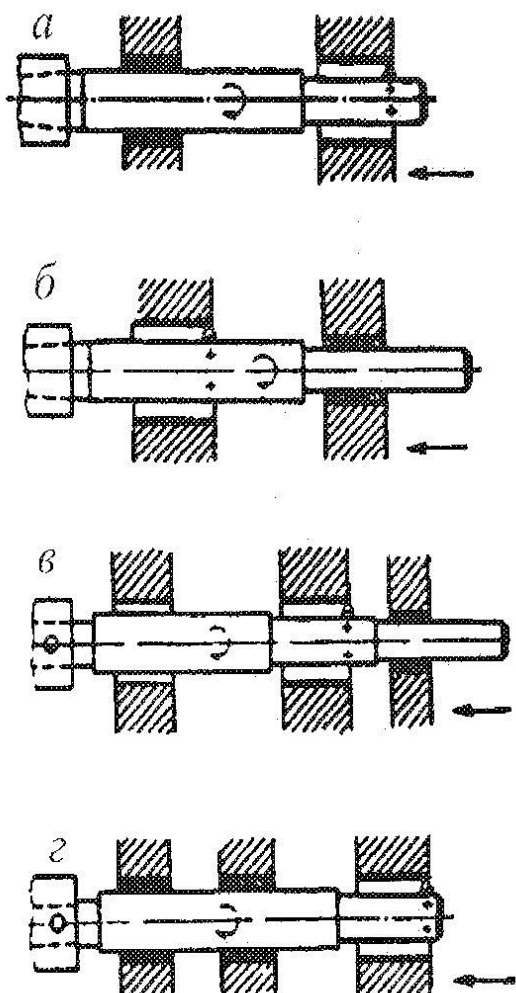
Схеми направлення інструмента кондукторними втулками
